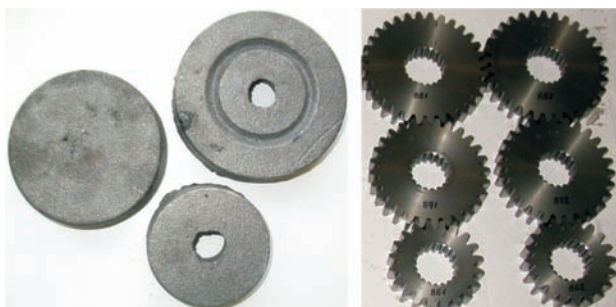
Литые заготовки и образцы зубчатых колес из высокопрочного чугуна
